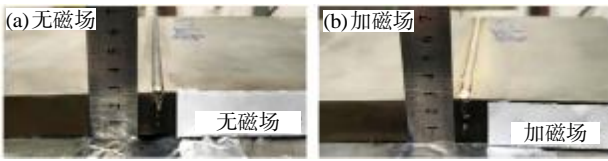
磁场辅助窄间隙激光填丝焊缝形貌
